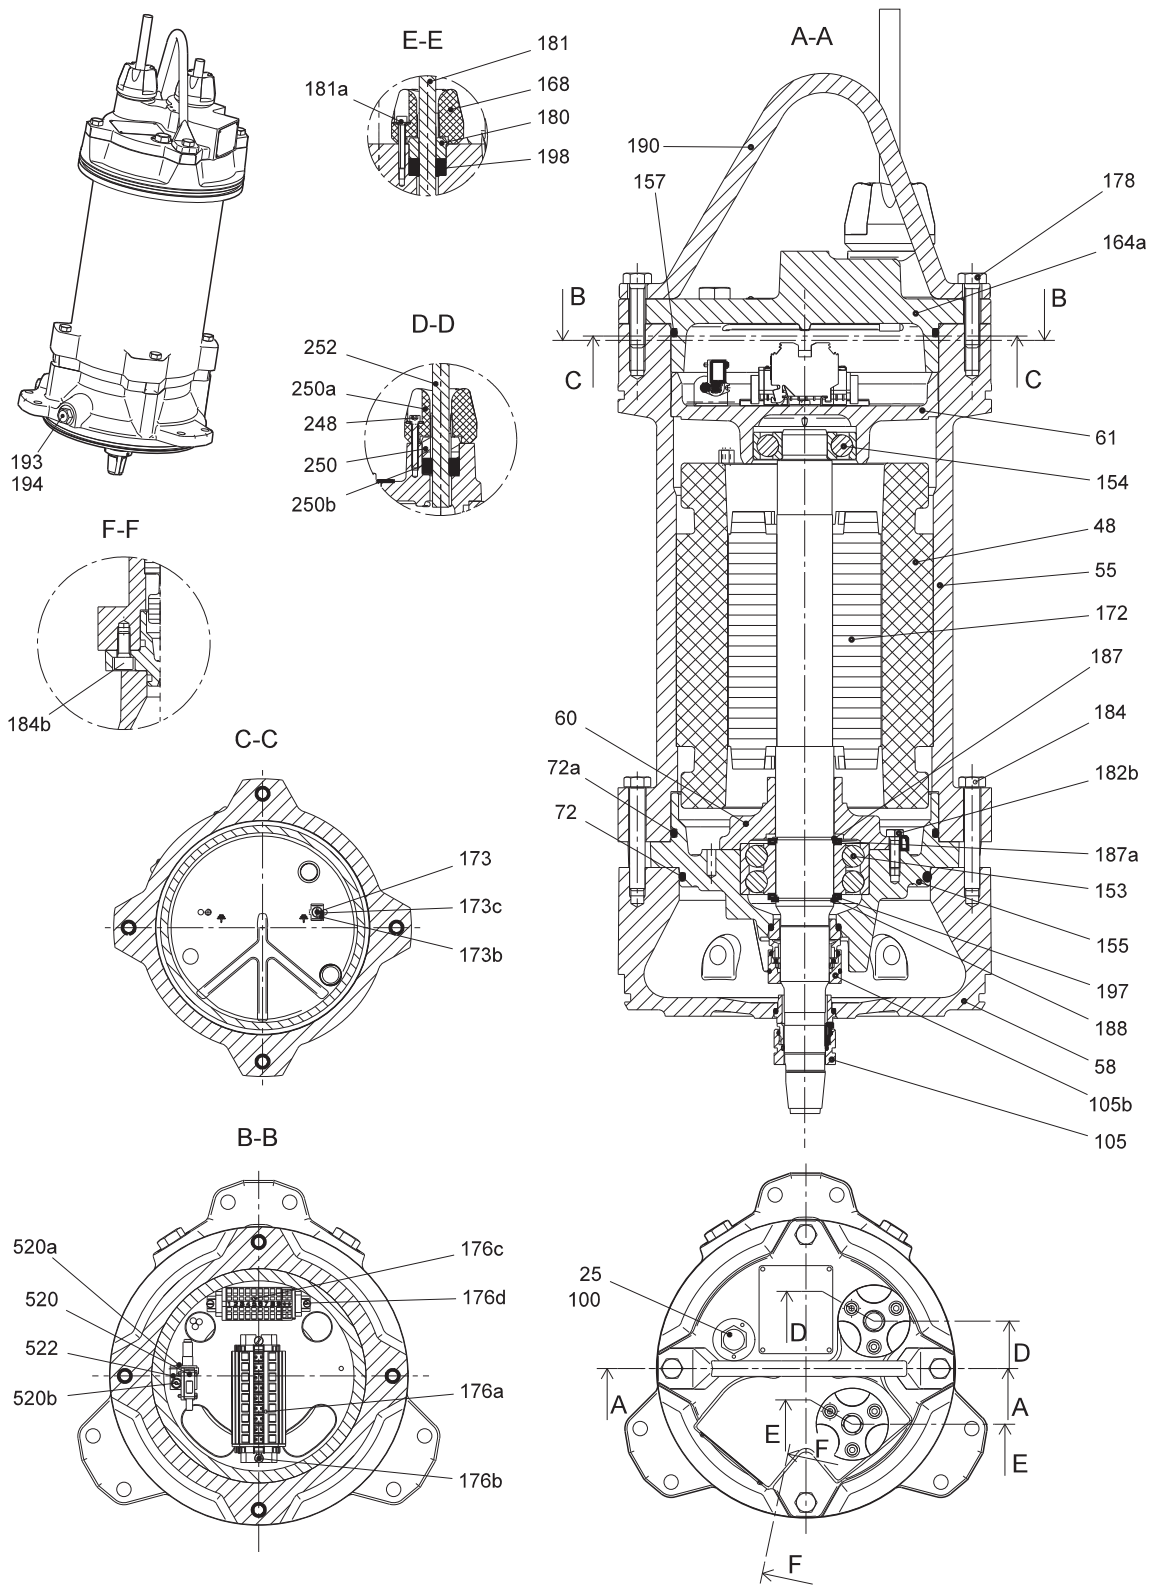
Невзрывозащищённые двигатели, без охлаждающего кожуха
